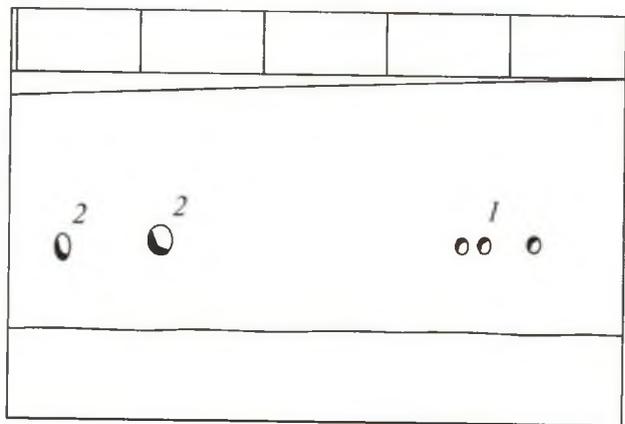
Цепочка пор – группа пор в сварном шве, расположенных в линии, в угловом сварном соединении штуцера с трубопроводом
